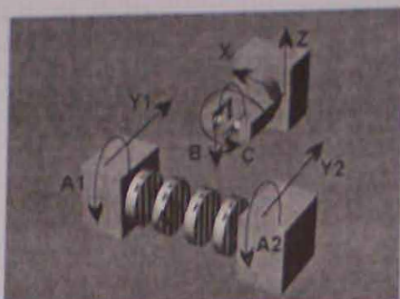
Soustružení na frézce - MAZAK INTEGREX e 1060V [5]
